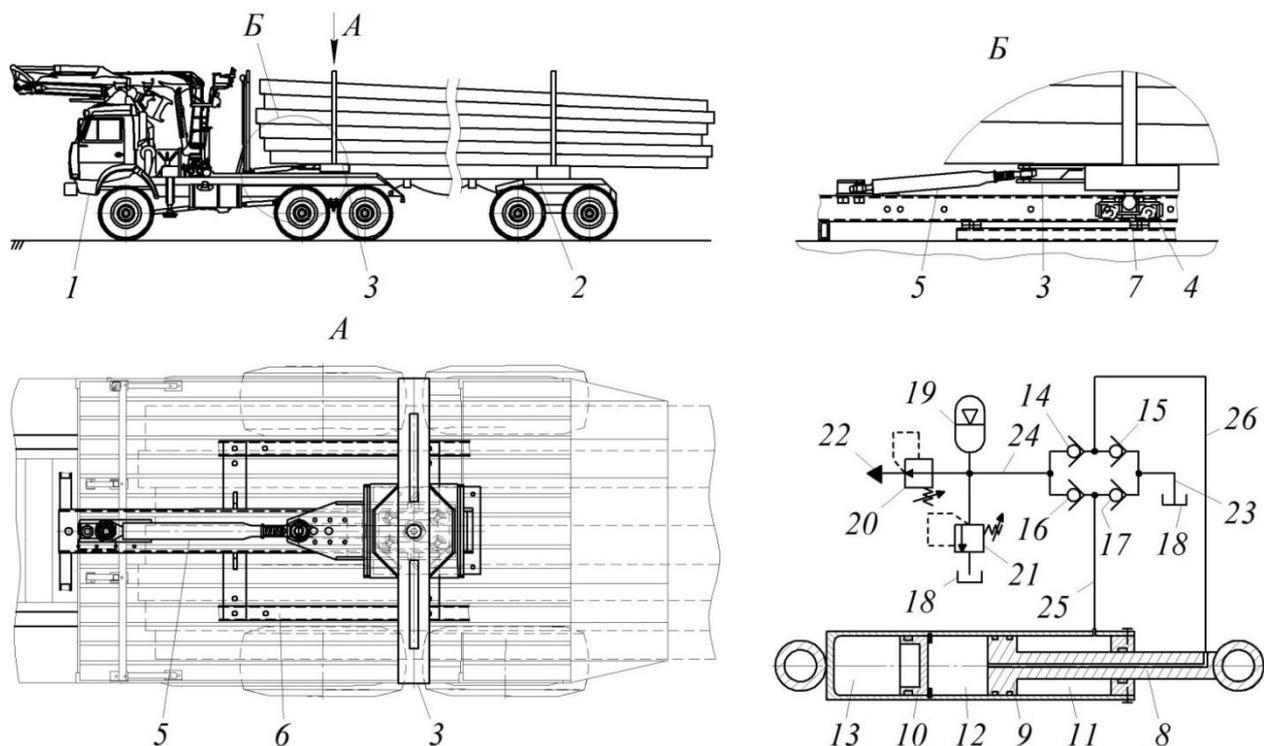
Схема рекуперативного поворотного коникового устройства с демпферным механизмом: 1 – лесовозный тягач; 2 – прицеп-ропуск; 3 – поворотный коник; 4 – механизм перемещения поворотного коникового устройства; 5 – гидроцилиндр; 6 – продольные лонжероны рамы; 7 – шаровая опора; 8 – шток; 9 – поршень; 10 – поршень газовой полости; 11, 12 – штоковая и поршневая полости; 13 – газовая полость; 14-17 – обратные клапаны; 18 – гидробак; 19 – пневмогидроаккумулятор; 20 – редукционный клапан; 21 – предохранительный клапан; 22 – порт подачи рабочей жидкости потребителю; 23 – всасывающий трубопровод; 24 – напорный трубопровод; 25, 26 – гибкие трубопроводы
